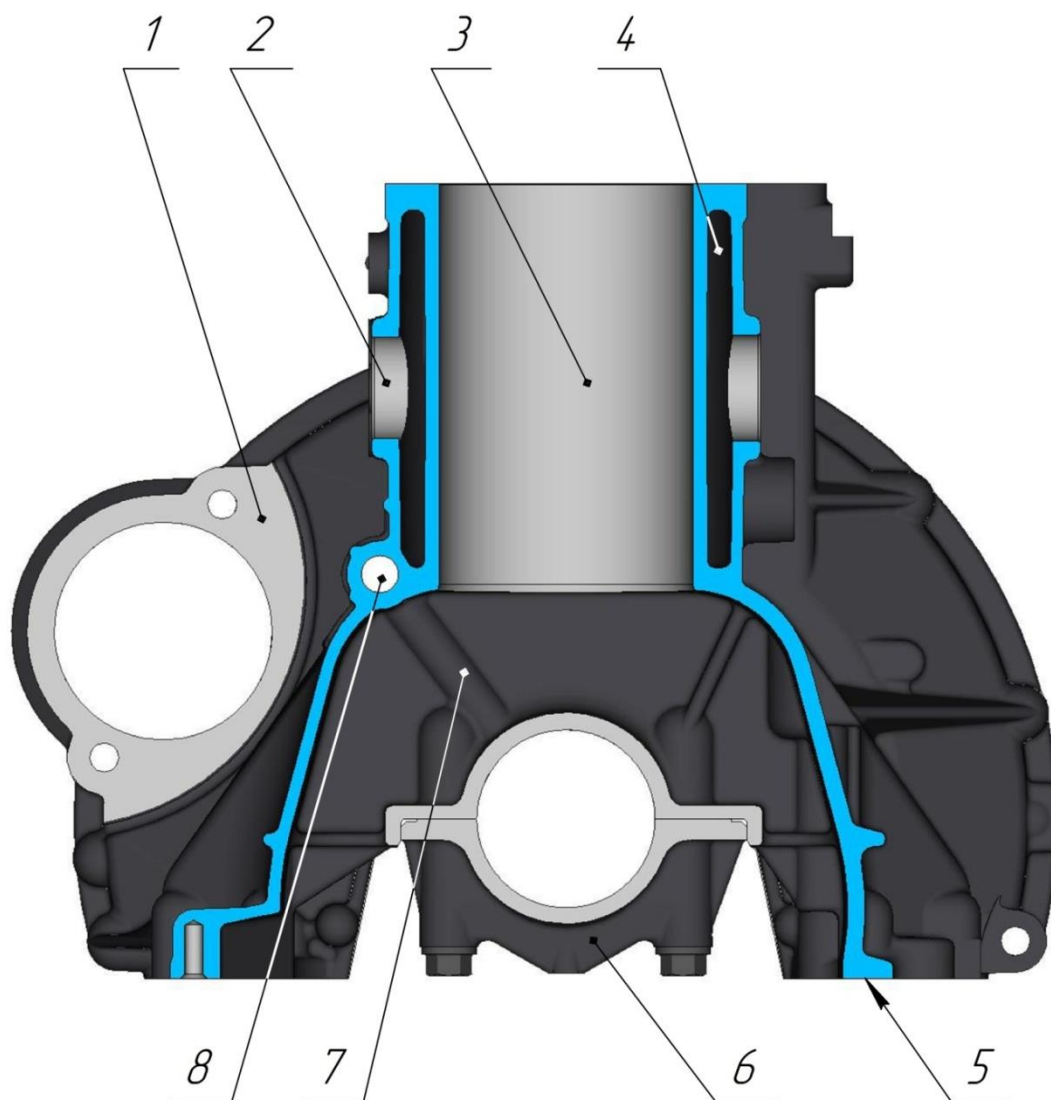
Блок цилиндров. Поперечный разрез по оси цилиндра:
